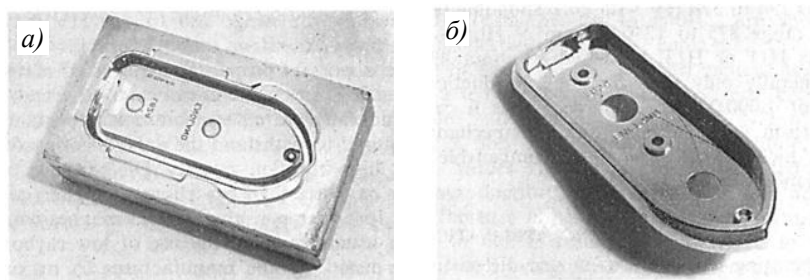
Матрица для литья под давлением (а) из сплава системы никель–кобальт, полученная методом гальванопластики, и пуансон, изготовленный из цинковой отливки (б)
